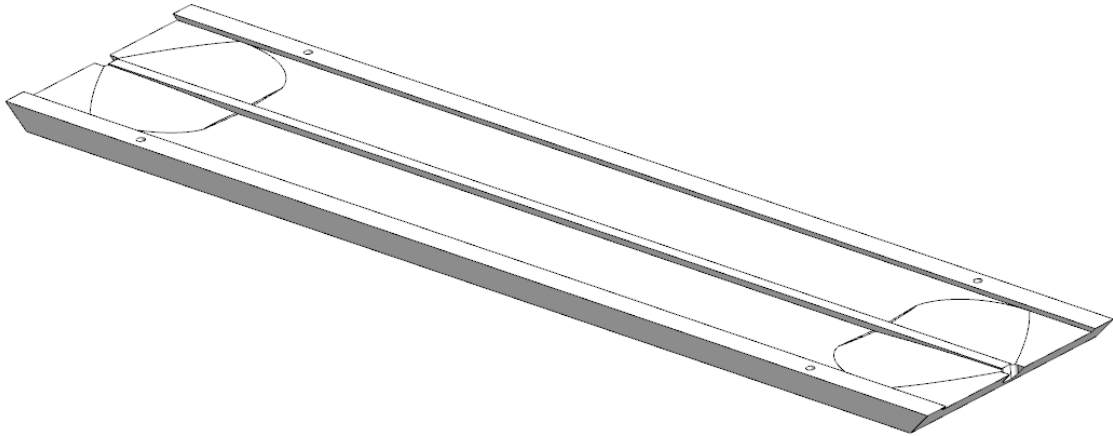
Placa de PE 1000. Conjunto de rotación. Mecanizado CNC.
